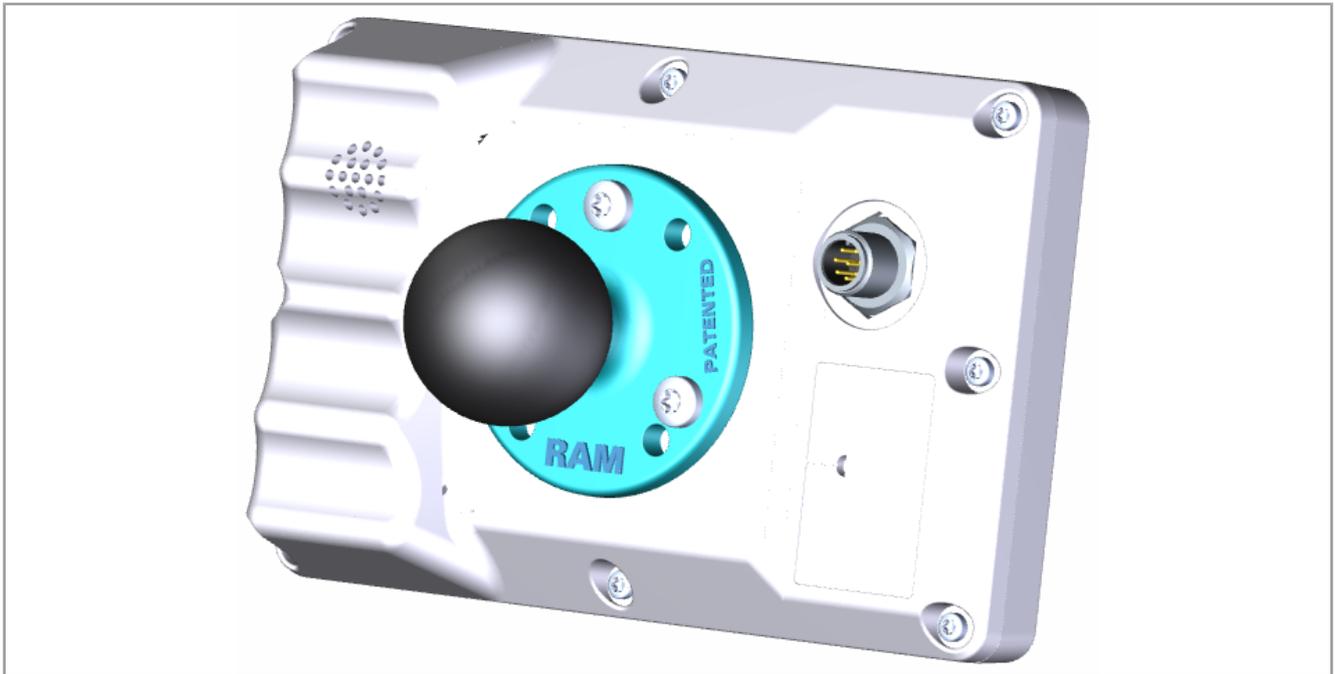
Erlaubte Einbaulage mit RAM-Mount-Halterung
